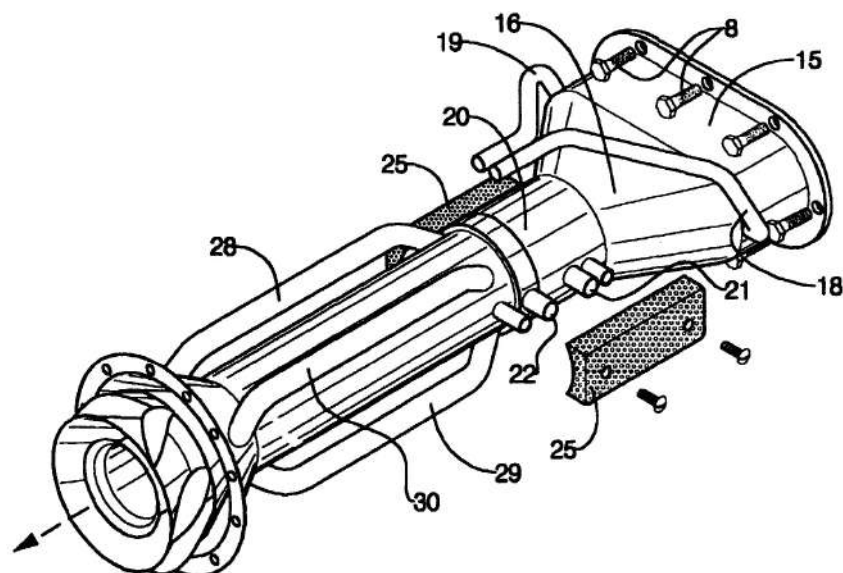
Загальний вигляд середньої частини пристрою
